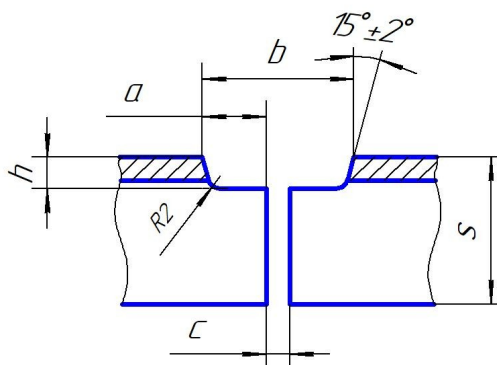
Разделка кромок листов двухслойных сталей при автоматической и ручной сварке с удалением защитного лакирующего слоя.
